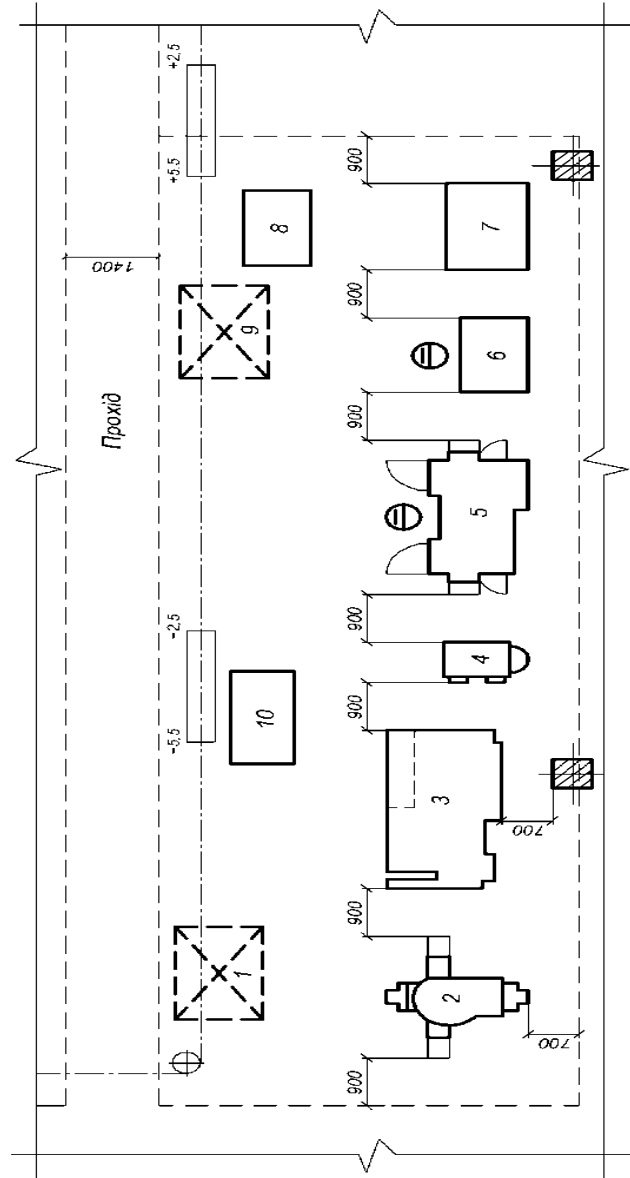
Приклад плану розміщення обладнання на дільниці механічної обробки: 1 – місце складування заготовок; 2 – вертикально-фрезерний мод.6Н10; 3 – токарний багаторізцевий півавтомат мод.1А720;
